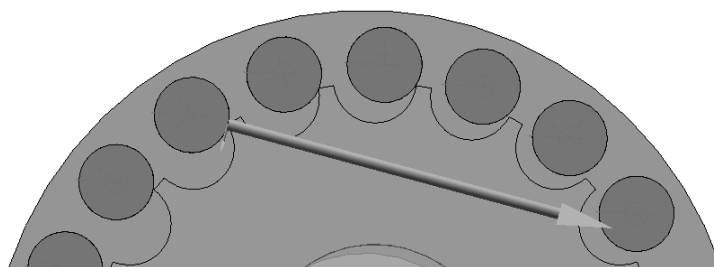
Сила в зацеплении роликов с зубьями сателлита эксцентриковой роликовой передачи
